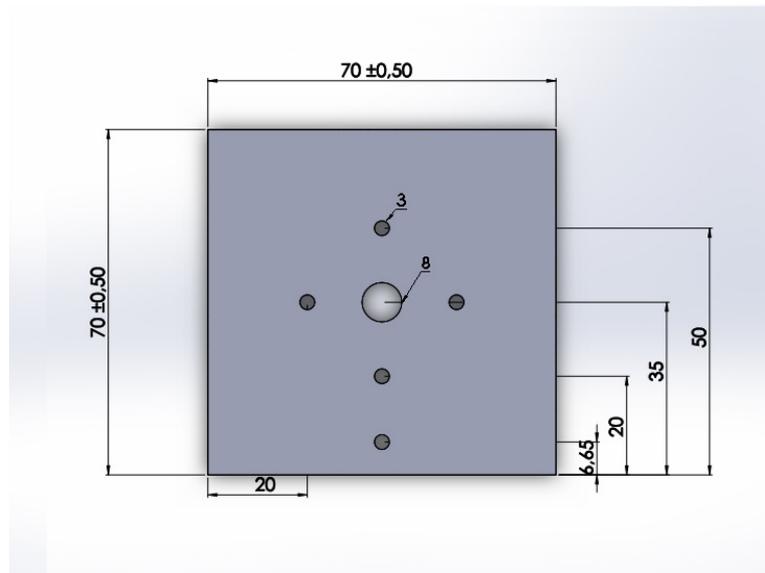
desenho técnico para auxiliar na construção do componente 11: placa base.
